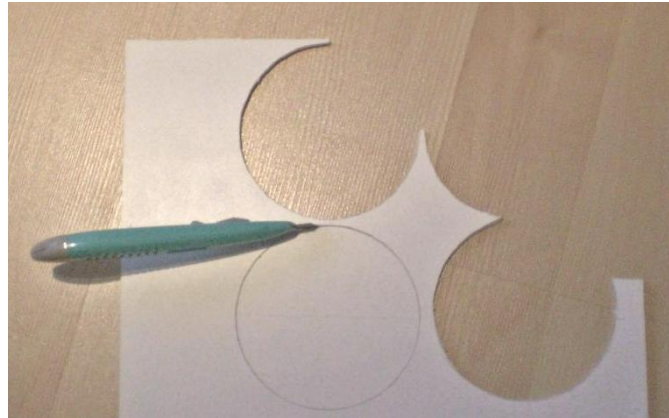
9: Corte de piezas de la plancha de PVC de 6 mm
